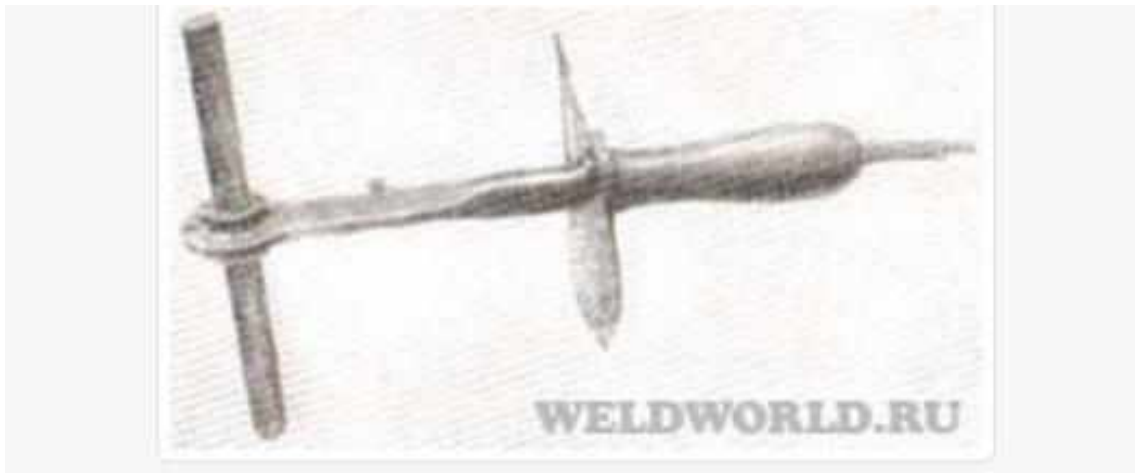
Porta eletrodo de carbono – Weldworld.ru
